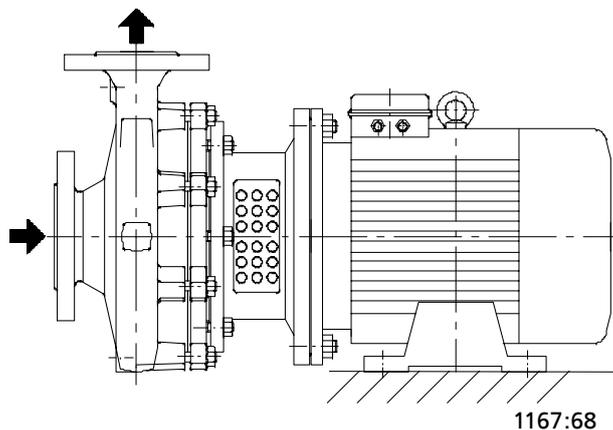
Fijación inferior del pie de motor abajo, desde el tamaño de motor 132 = 5,5 kW hasta 225 = 45 kW
